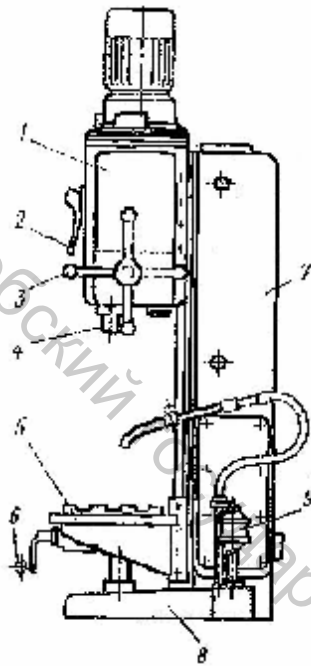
Общий вид вертикально-сверлильного станка мод. 2H135
